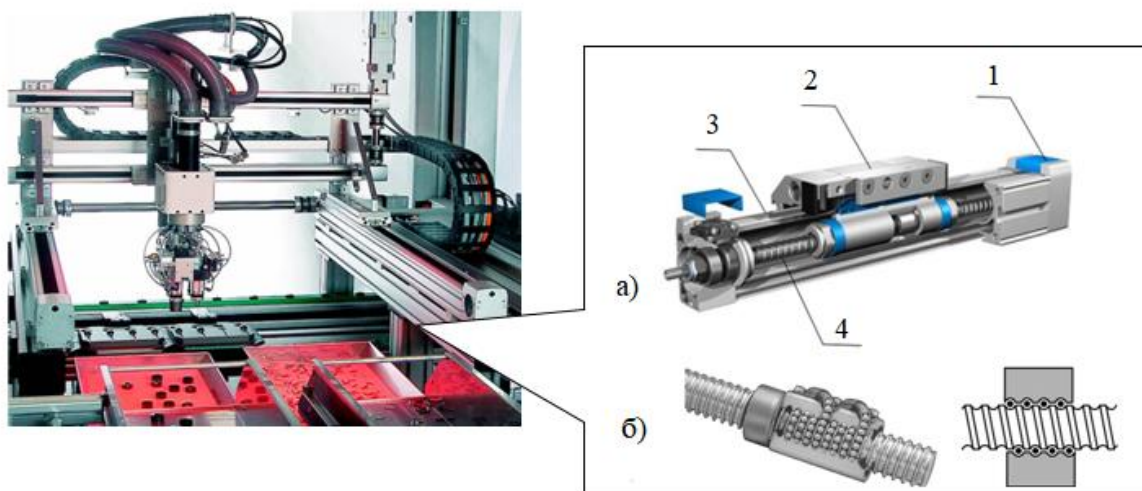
«Ось» з передачею «гвинт-гайка» а): 1 – корпус; 2 – напрямна; 3 – каретка; 4 – передача «гвинт-гайка»; б) конструкція з елементами підшипників кочення
